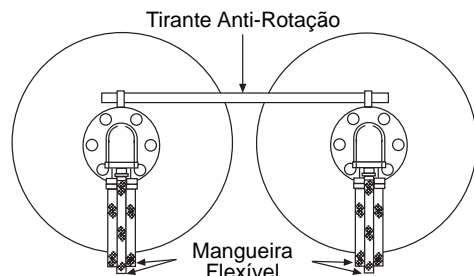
Instalação horizontal do tirante nas orelhas do corpo.
